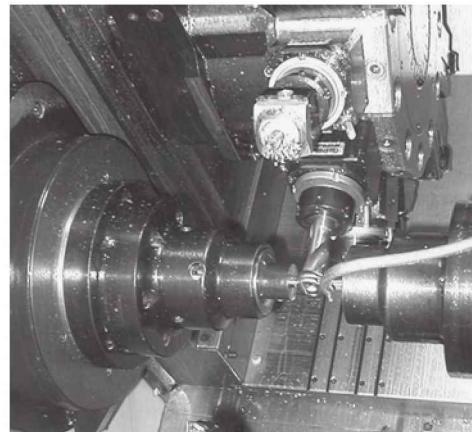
Os acessórios das ferramentas rotativas permitem operações de fresagem usando um torno.
